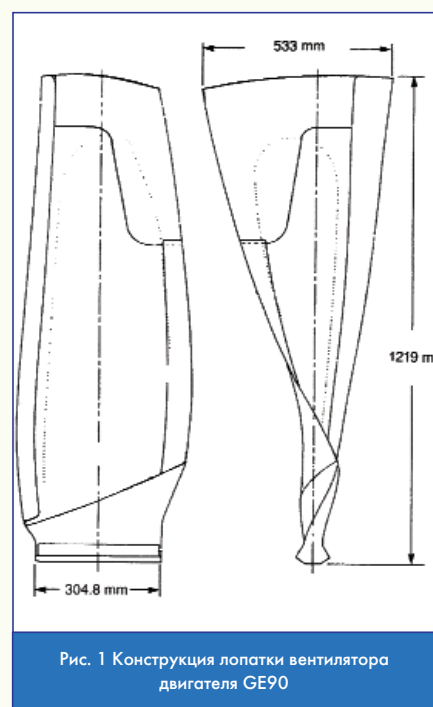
Конструкция лопатки вентилятора двигателя GE90
